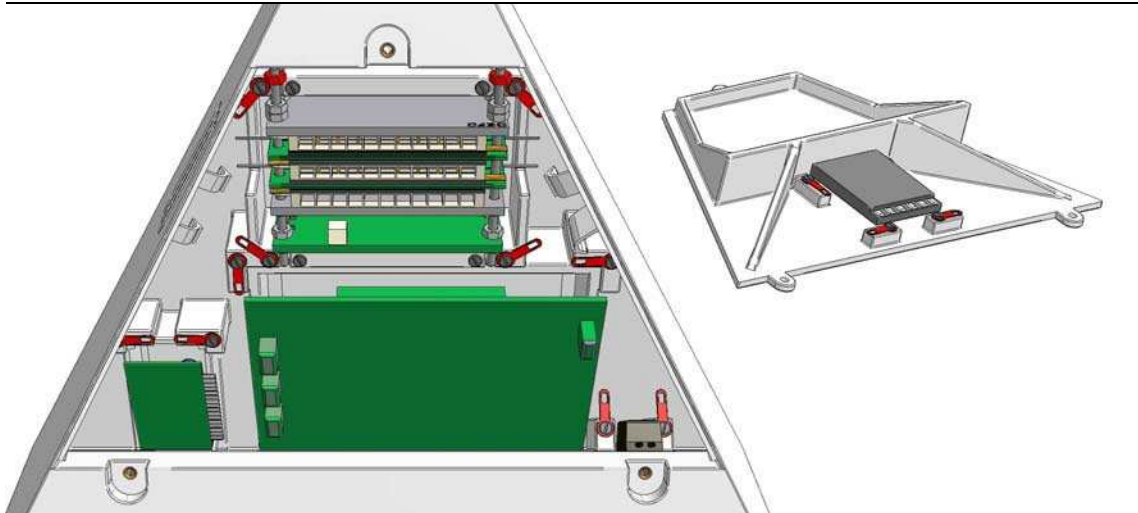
Befestigung der Komponenten im offenen Zustand
